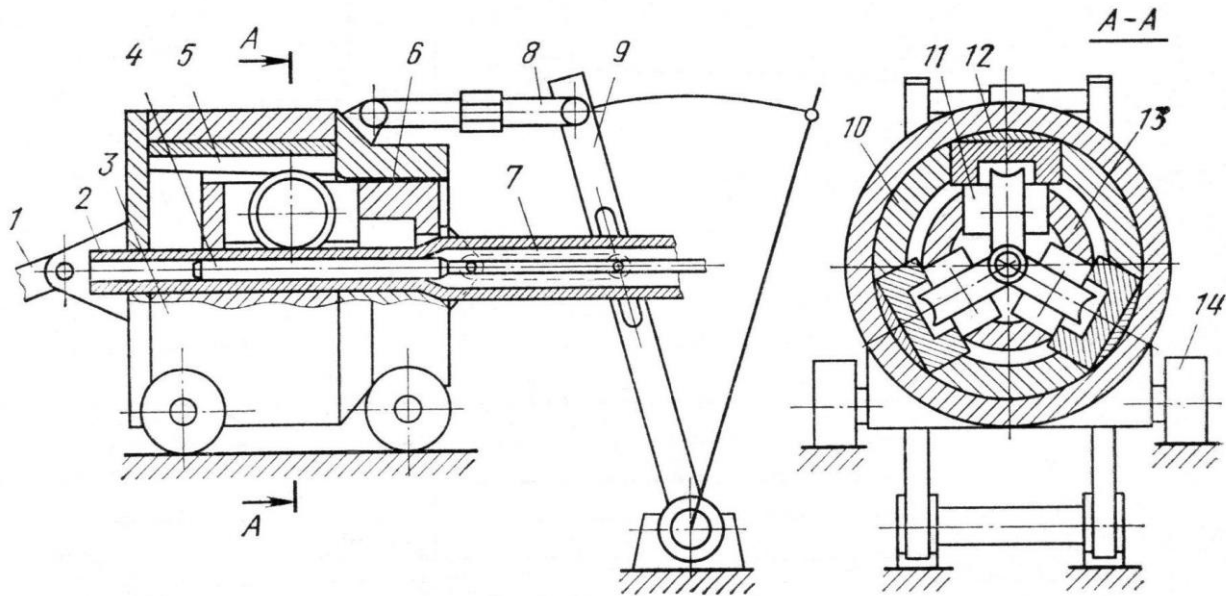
Принципова схема кліті для стану ХПТР конструкції ВНДІМЕТМАШ: 1 – шатун кривошипно-шатунного дезаксіального приводу; 2 – готова труба; 3 – товстостінний корпус (гільза); 4 – циліндрична оправка; 5 – опорна планка; 6 – повзун; 7, 8 – шарнірні тяги; 9 – куліса; 10 – труба; 11 – ролик з опорними цапфами; 12 – регулювальні клини; 13 – сепаратор для роликів; 14 – ходові катки.
